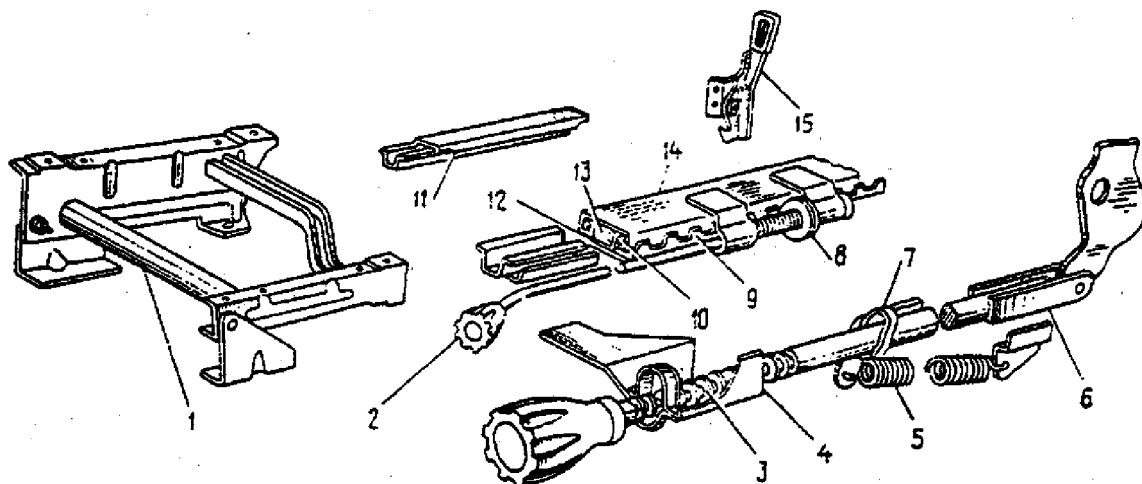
Mecanismos de regulagem do banco dianteiro: 1 - suporte do assento; 2 - manopla do mecanismo de posicionamento; 3 - haste com rosca helicoidal para regulagem da inclinação do encosto; 4 - fixador da inclinação do encosto; 5 - mola; 6 - haste; 7 - dispositivo de retenção; 8 - dobradiças do dispositivo de trava; 9 - dispositivo de trava; 10 - esfera; 11 - canaletas de deslizamento; 12 - guias dos trilhos; 13 - rolete; 14 - trilho; 15 - trava do assento.
